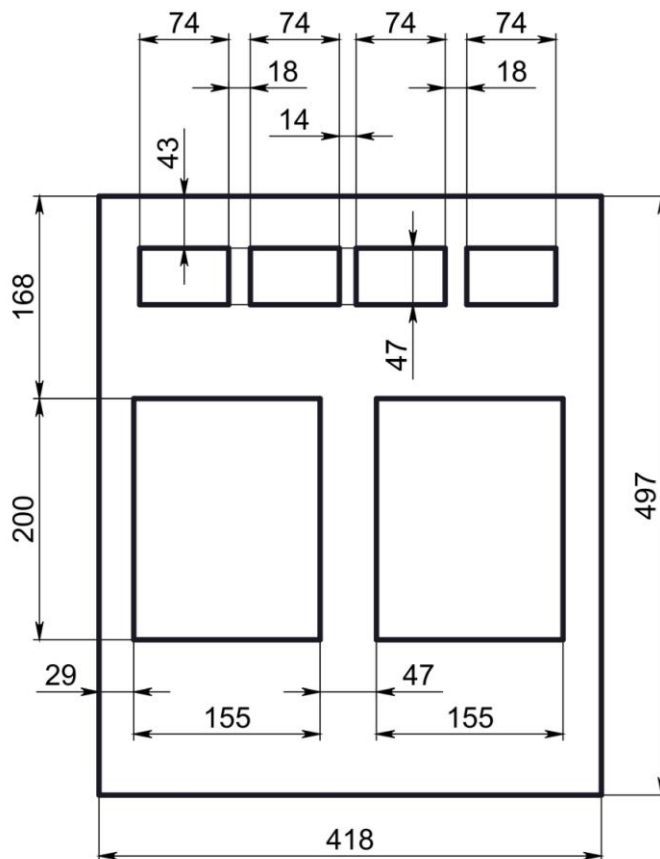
Габаритные, установочные и присоединительные размеры
